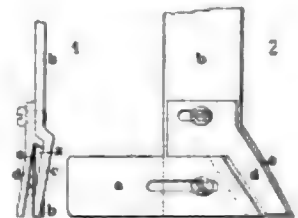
Werkzeug zum Abschärfen von Lederkanten.
